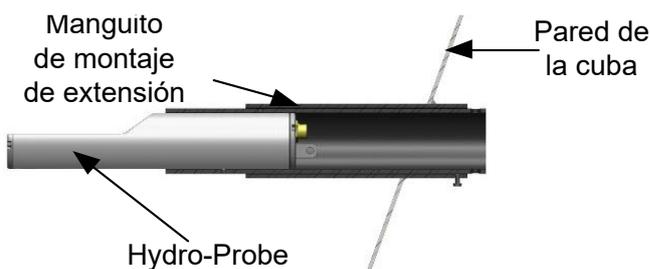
Hydro-Probe instalado en un manguito de montaje de extensión
